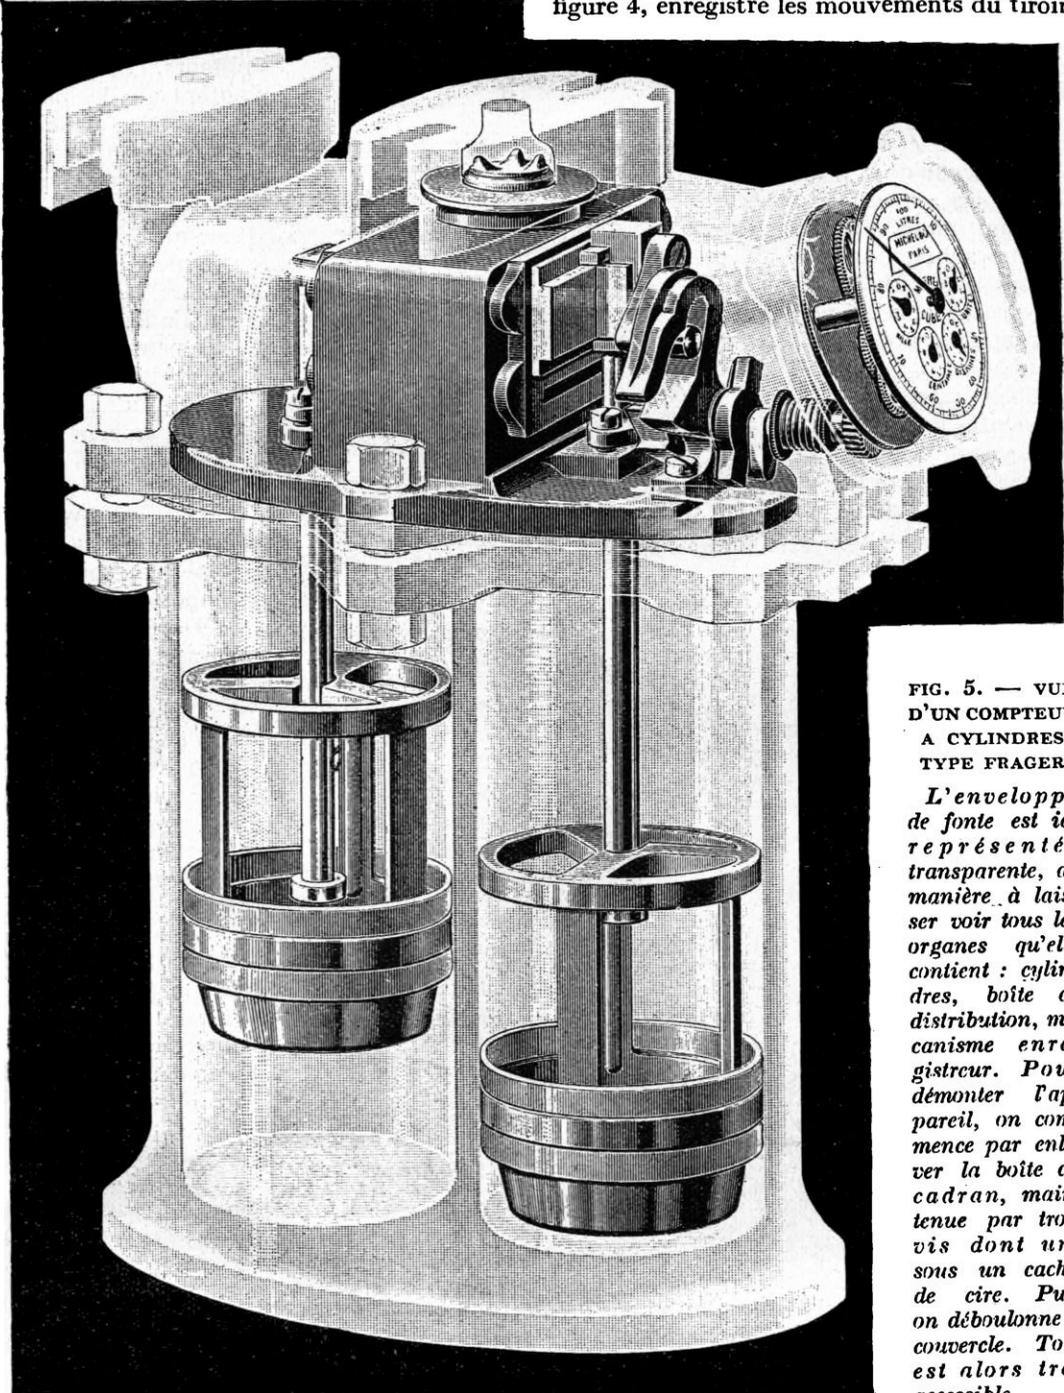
VUE D'UN COMPTEUR A CYLINDRES TYPE FRAGER
